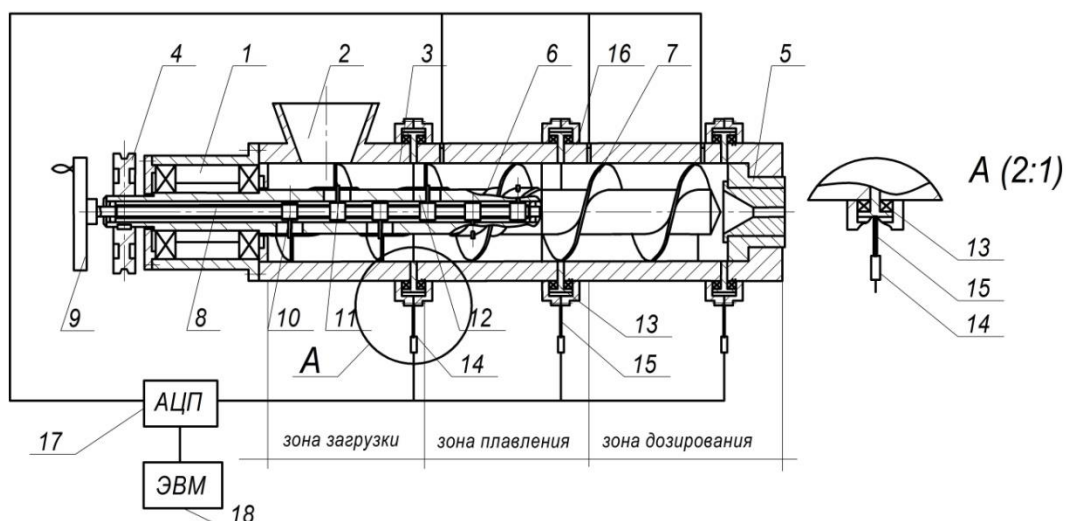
Схема установки с автоматическим контуром управления для экструдирования кормовых продуктов: 1 – подшипниковый узел, 2 – загрузочная воронка, 3 – разъёмные корпуса шнековой камеры, 4 – привод, 5 – формующая головка, 6 – шнек, 7 – витки шнека, 8 – резьбовой вал, 9 – приводной механизм, 10 – втулки с установленными пальцами 11, 12 – направляющие, выполненные в теле шнека, 13 – цилиндрическая вставка, 14 – тензодатчики, 15 – гибкие элементы, 16 – датчики температуры, 17 – аналого-цифровой преобразователь, 18 – компьютер.
